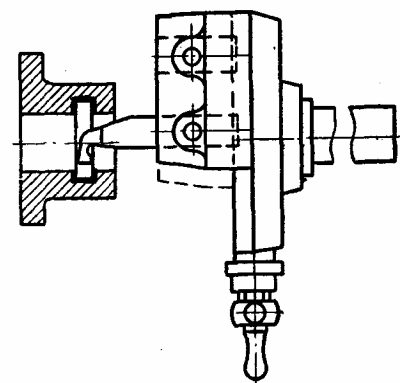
Подвижной суппорт для протачивания внутренней канавки с ручной подачей
